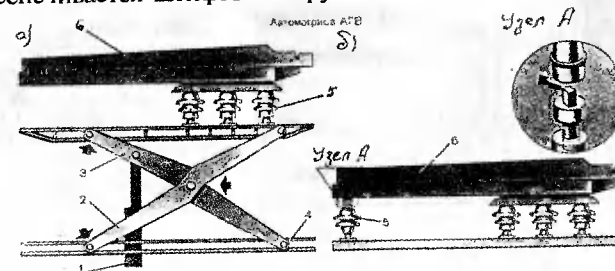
Механизм подъема рабочей площадки (а); механизм поворота рабочей площадки автомотрисы АГВ (б):
